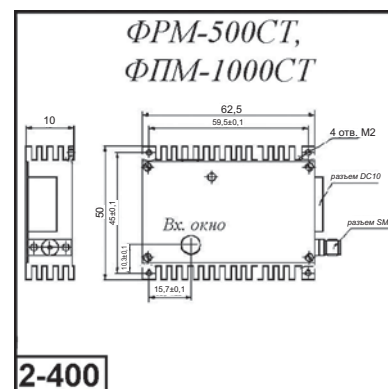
Внешний вид и габаритные размеры ФПУ типа ФПМ-500СТ и ФПМ-1000СТ
